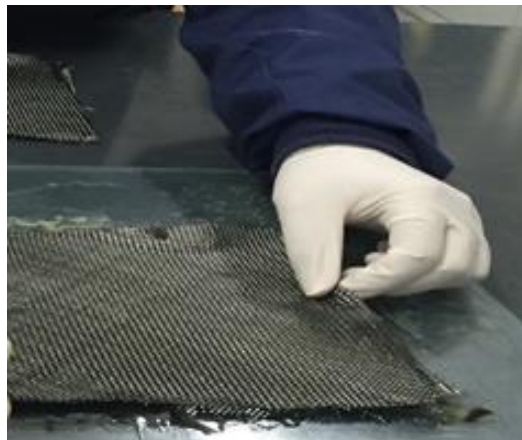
Corte de fibra de carbono para la manufactura de probetas.
